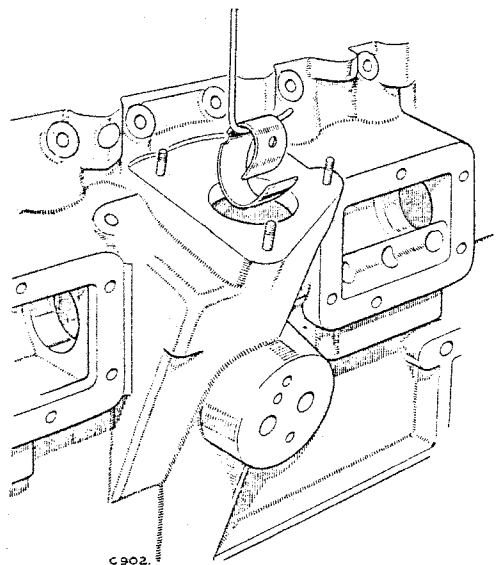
Desmontaje del cojinete interior del árbol de levas.
